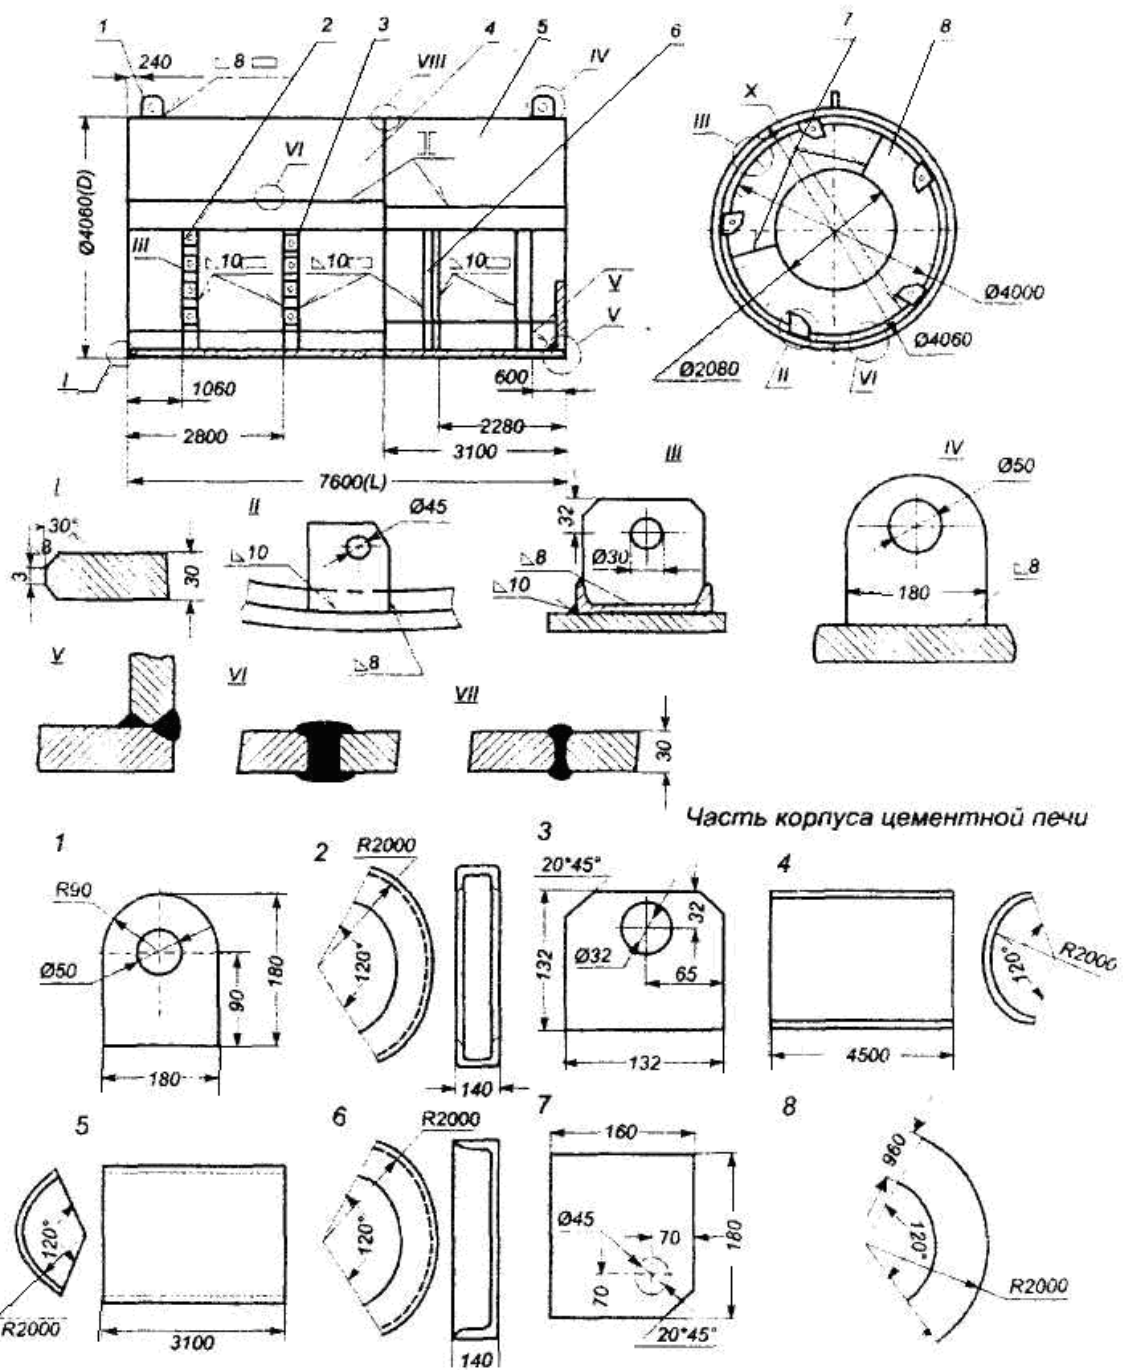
Эскизы корпуса цементной печи и ее детализовки для задания № 2
